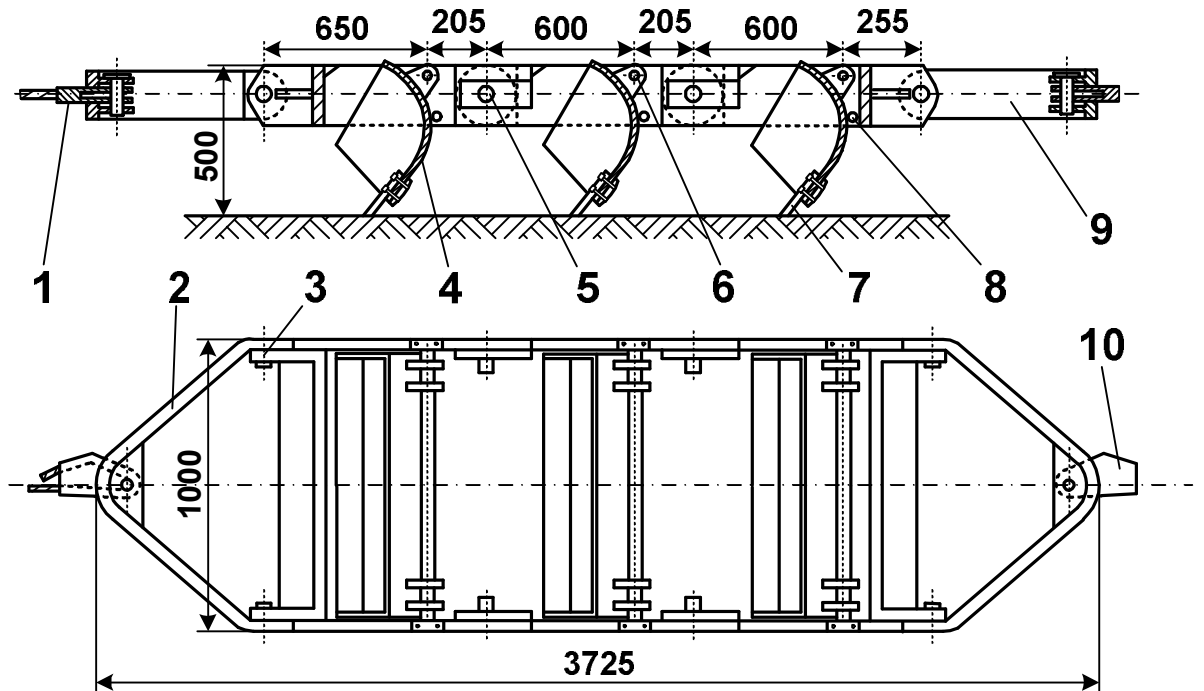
Многоковшовый шарнирно-складывающийся скрепер:
